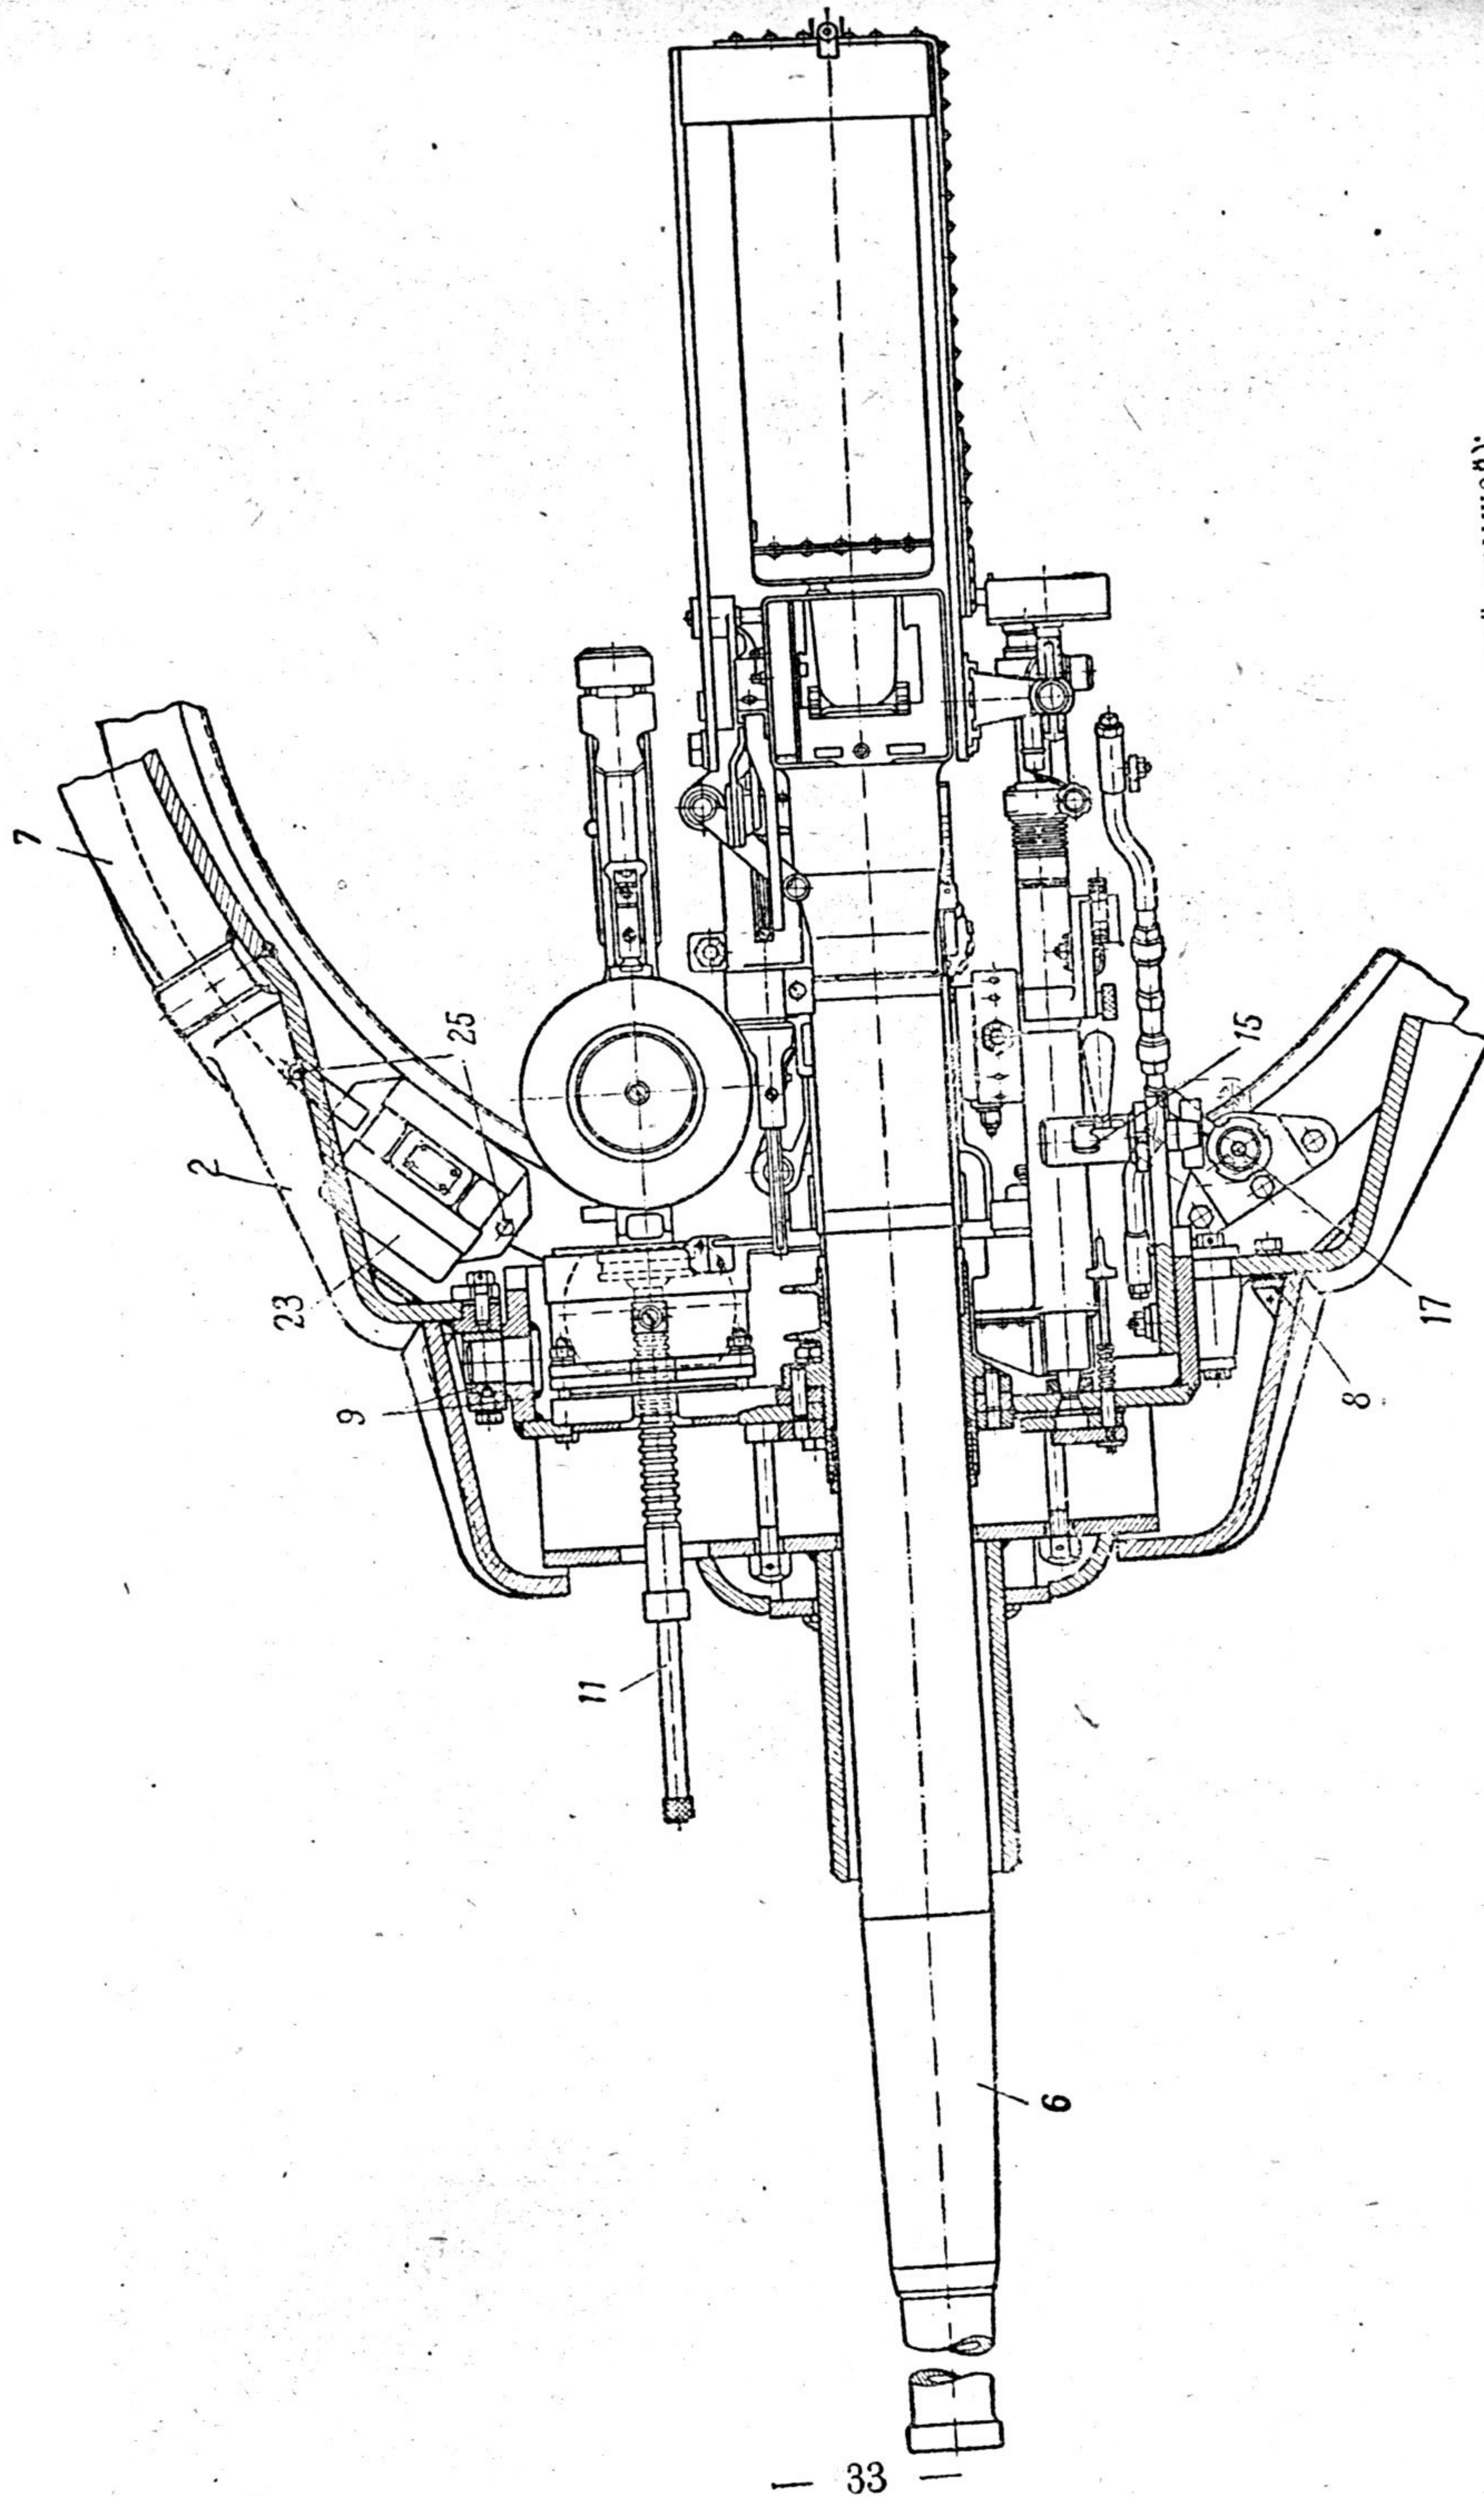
Вид сверху на башню со штампованным лобовым щитом (со снятой крышкой): 2 — передний лист корпуса; 6 — крюк; 7 — бортовой лист башни; 8 — стальной фланец; 9 — подшипник; 11 — пулемет; 15 — стопор пушки; 17 — стопор башни; 23 — гидро- мотор прибора 70°; 25 — болты
